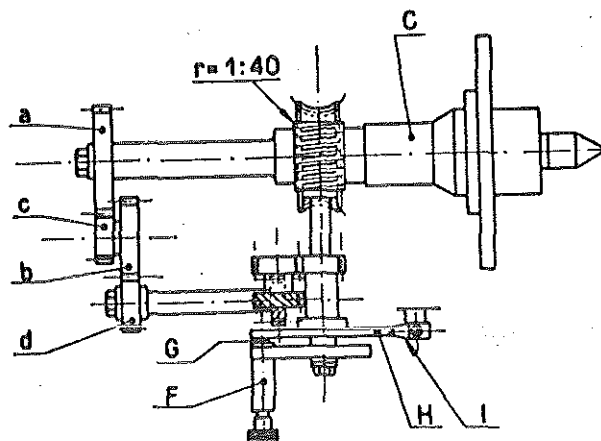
Divisor para fresadoras e cadeia cinemática.
